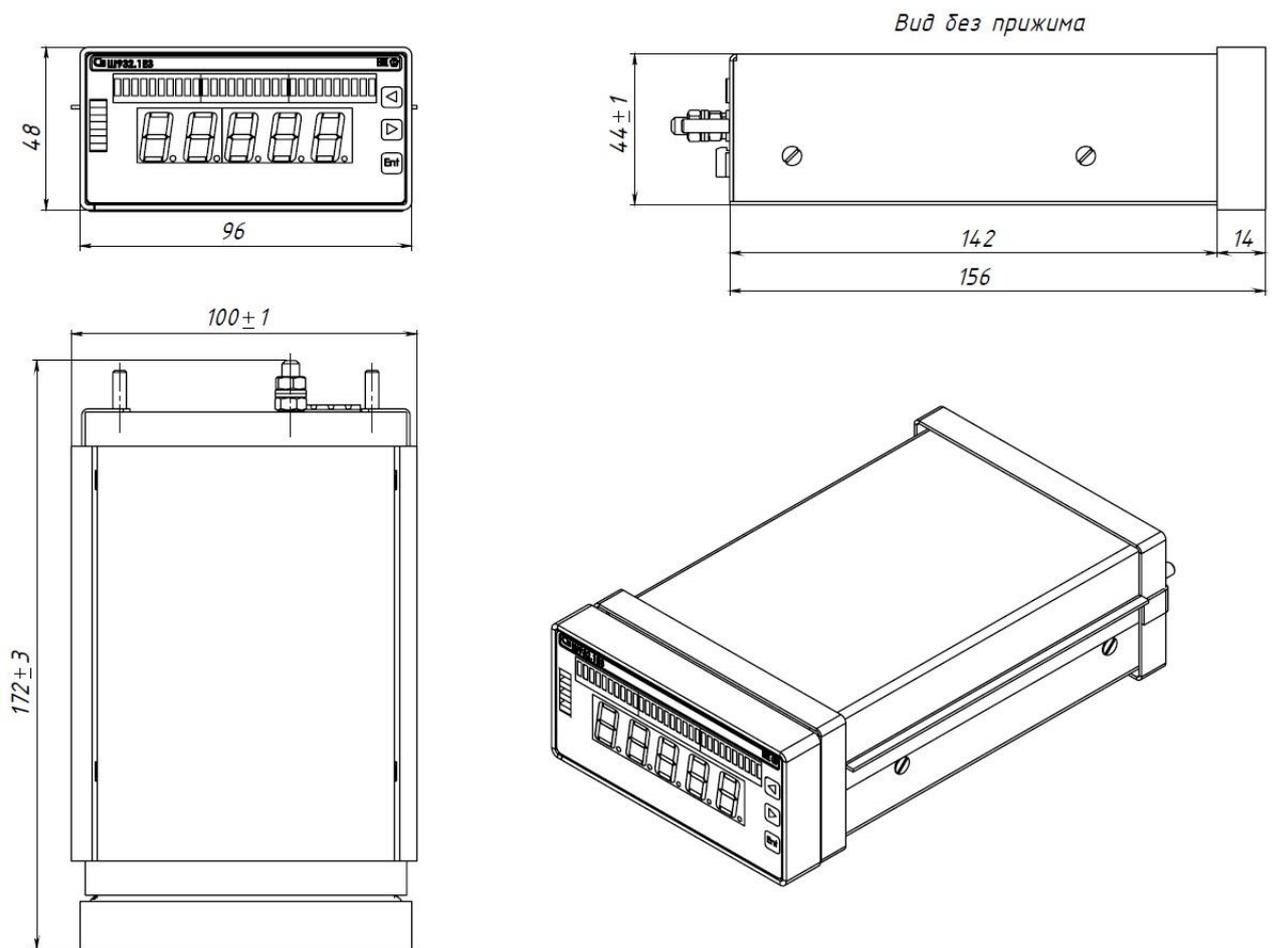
Габаритные и установочные размеры прибора Ш932.1Е3
